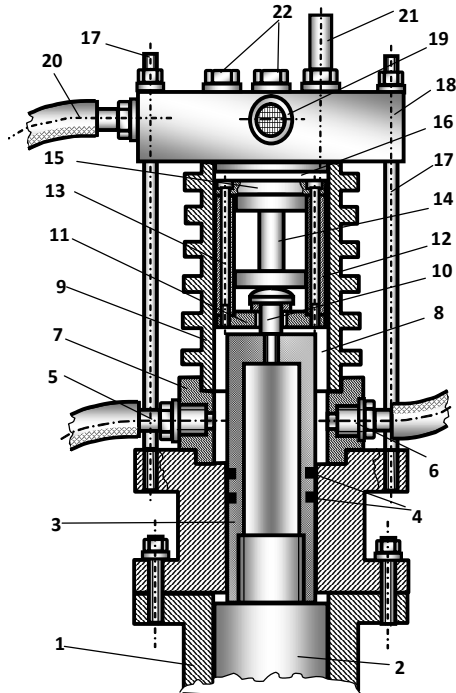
Конструктивная схема цилиндропоршневой группы модельного образца насос-компрессора при положении поршня близком к верхней мертвой точке:
